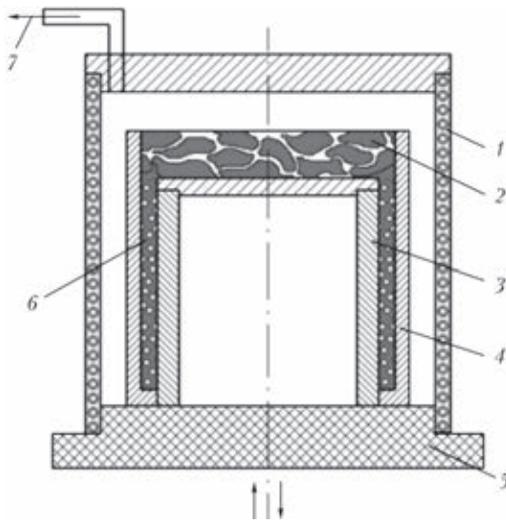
Схема индукционной печной наплавки (метод пропитки): 1 — индуктор, 2 — материал для связки композиционного сплава (мельхиор); 3 — деталь для наплавки; 4 — технологическая оболочка; 5 — под печи; 6 — наплавленный композиционный сплав; 7 — система откачки вакуума
